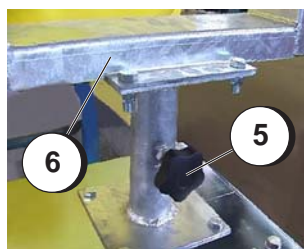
BWS 130-PE - mit stufenloser Einstellung
